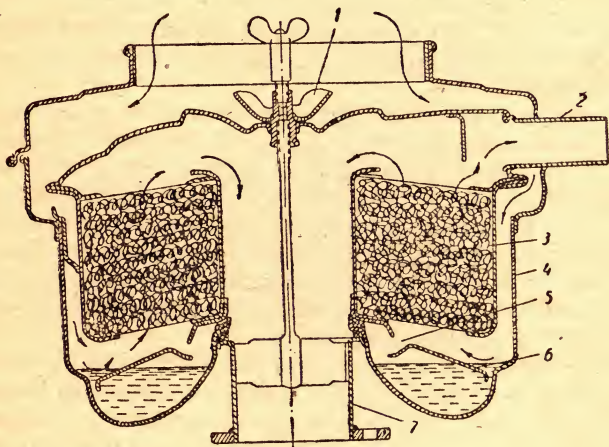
Воздушный фильтр ВМ-16 двигателя ЗИЛ-130
